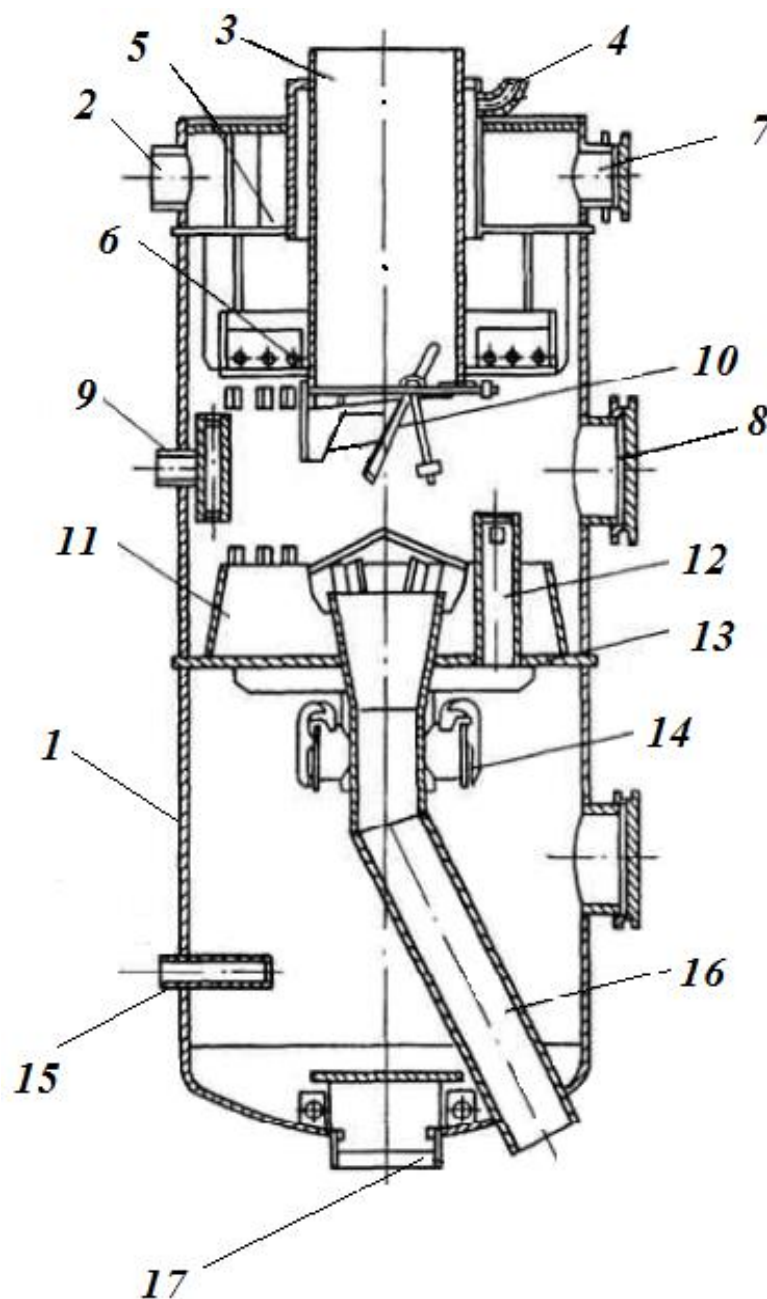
Конструктивная схема вертикального подогревателя низкого давления смешивающего типа [3]:
